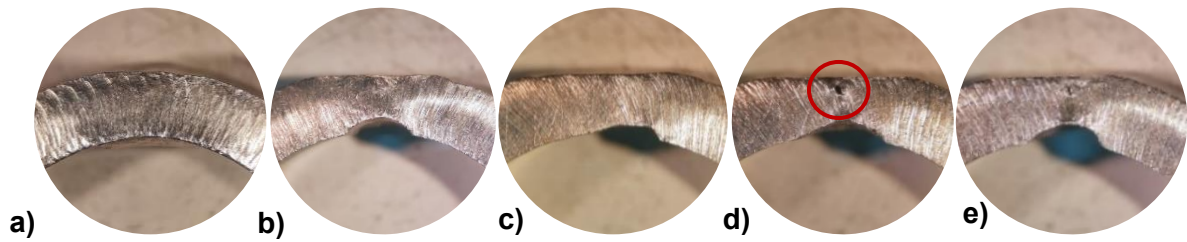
Ensayo de doblado en soldaduras AISI 304 sin material de aporte: a) Referencia; b) 115 A; c) 120 A; d) 125 A; e) 130 A.
